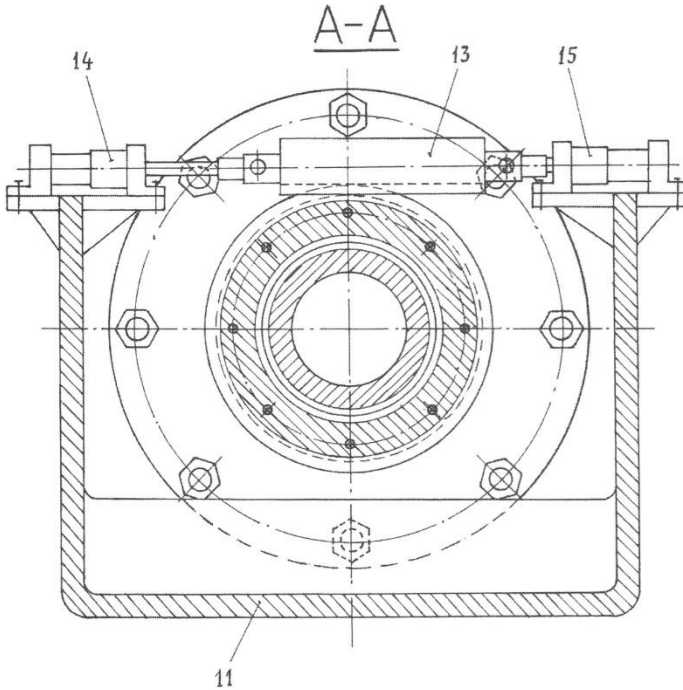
Розріз по А-А на рис. 3: 1 – корпус; 13 – зубчата рейка; 14 – лівий гідроциліндр; 15 – правий гідроциліндр; 16 – храпове колесо; 18 – кармани; 19 – планшайба; 20 – пружина; 21 – різьбова пробка.
